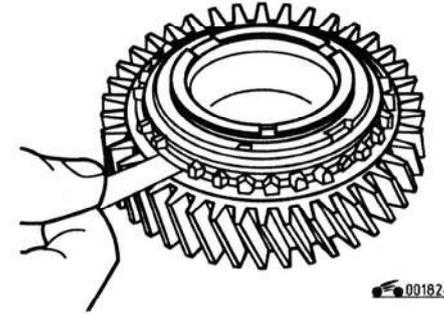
Проверка внешнего кольца синхронизатора II передачи
